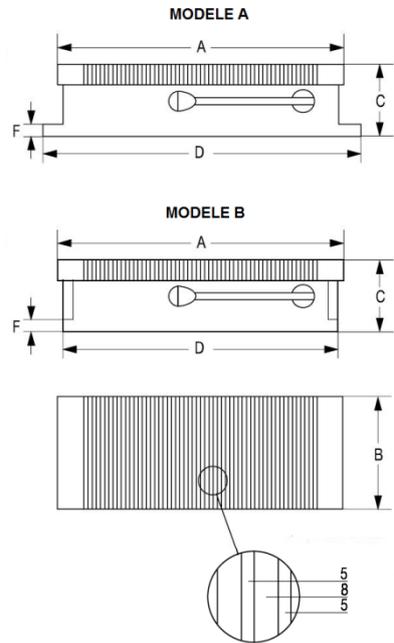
## PLATEAU MAGNETIQUE DE FRAISAGE – FERRO-MILL
